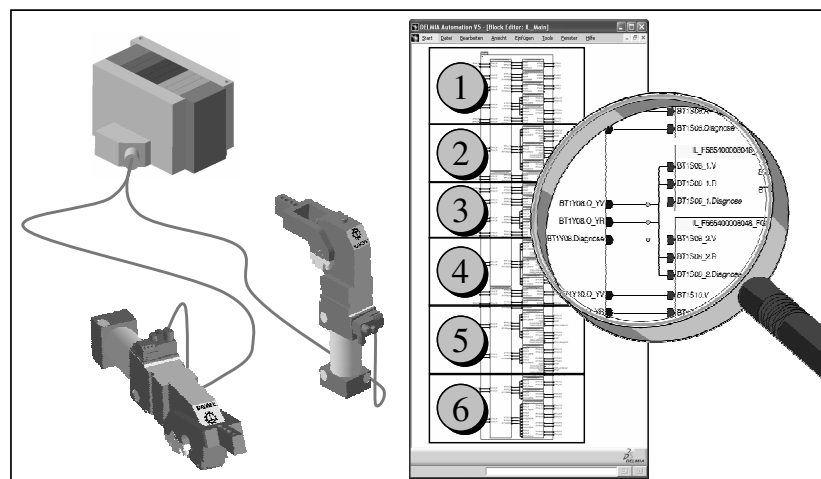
Spanner-Ventil-Verschaltungen der MAG-Schweißzelle 6 (Gesamtübersicht)
